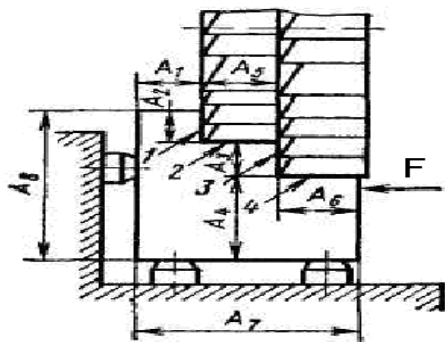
Схема обробки поверхонь заготовки (до задачі 1.4)
